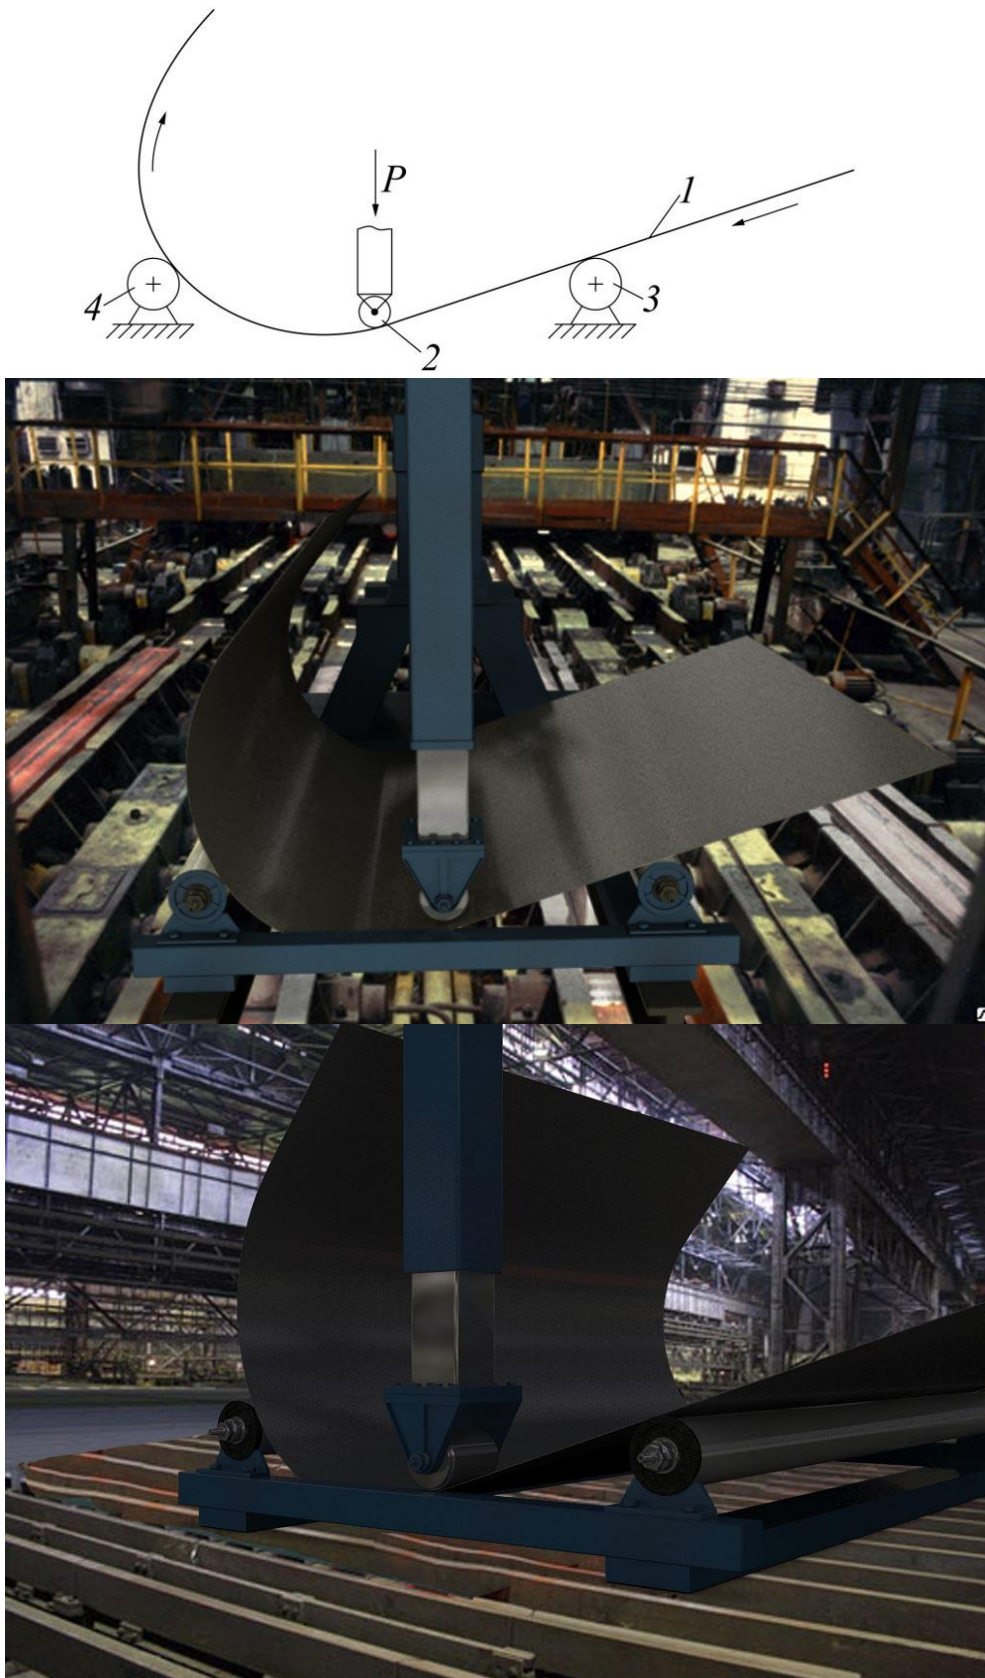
Схема упругопластического изгиба при шаговой формовке труб: 1 – лист; 2 – изгибающий (формующий) ролик; 3,4 – опорные ролики
